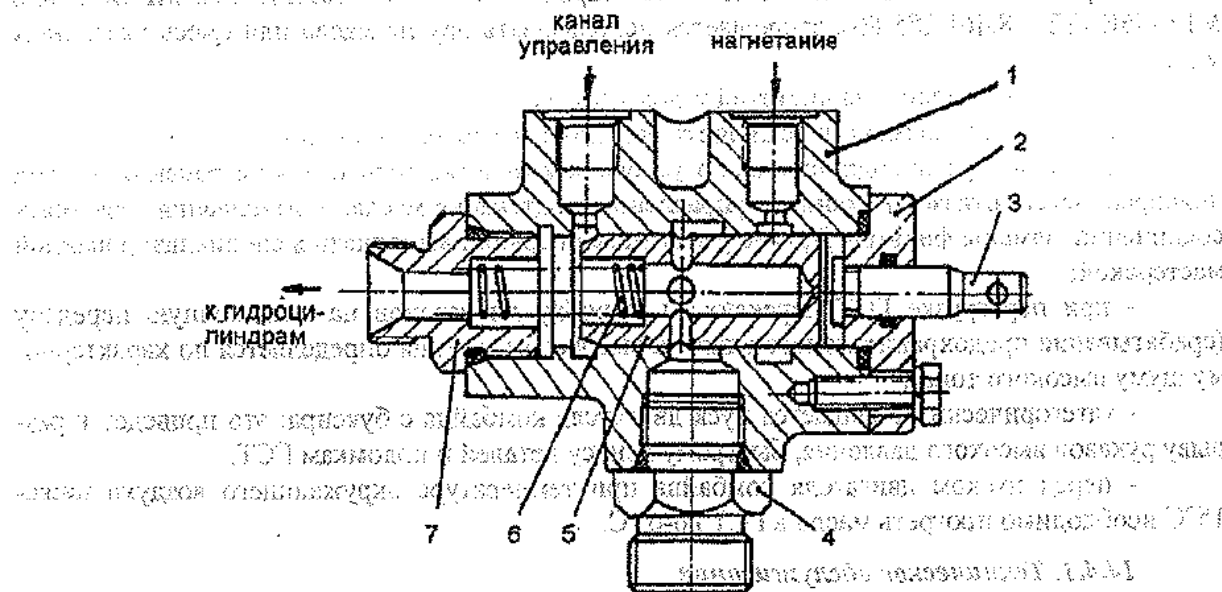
Распределитель копнителя: 1-корпус; 2-крышка; 3-толкатель; 4, 7-штуцеры; 5-золотник; 6-пружина
